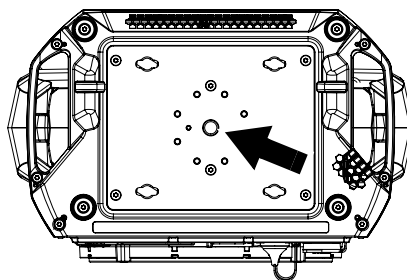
M12 Schraube für einzelne Befestigungsklemme
